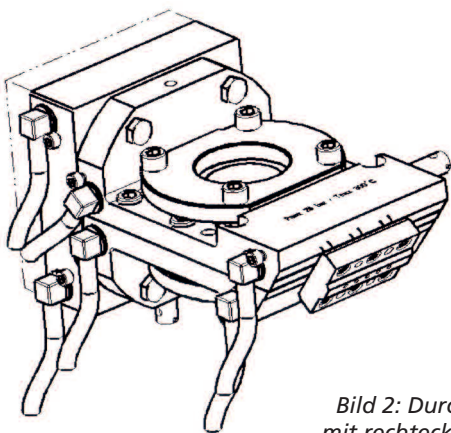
Durchlichtwerkzeug mit rechteckigem Fließkanal
